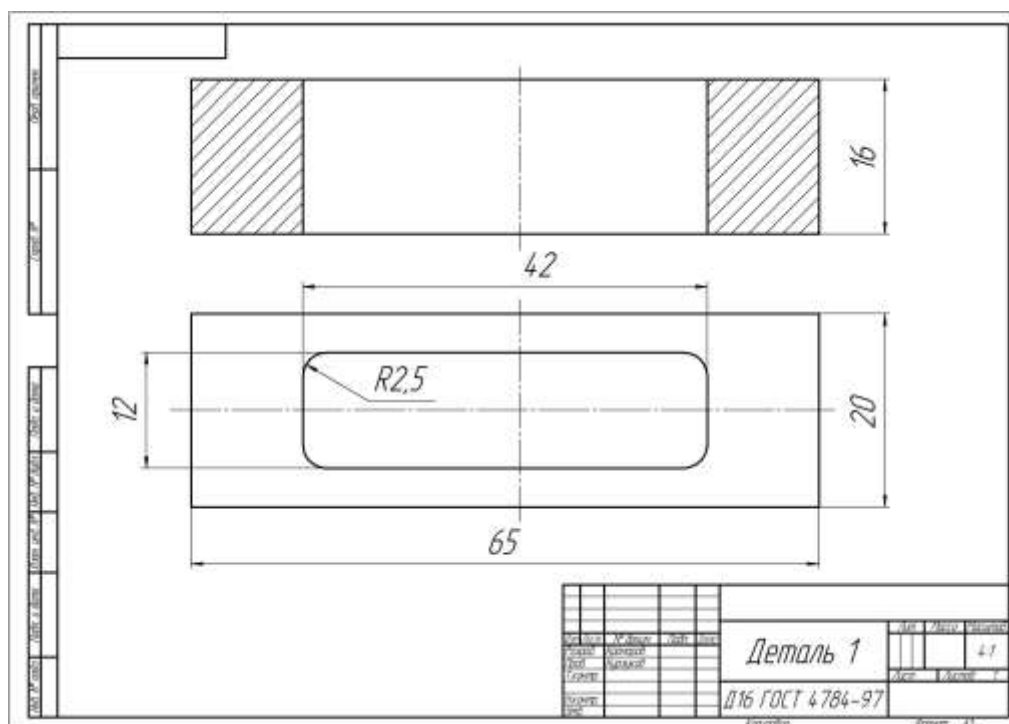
Чертёж детали, изготавливаемой на фрезерном станке BF20CNC
